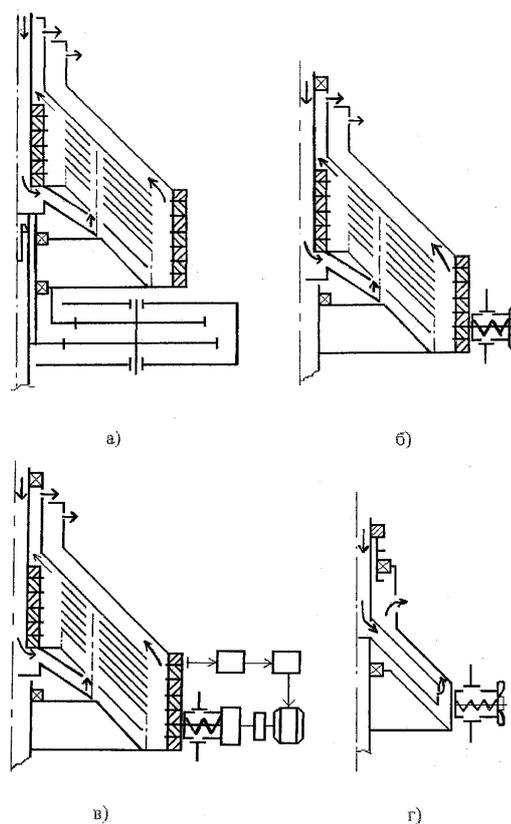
Кинематические схемы барабанов реосепараторов: а) разделителя с редуктором; б) разделителя с тормозом; в) разделителя с САР; г) очистителя с регулятором зазора
